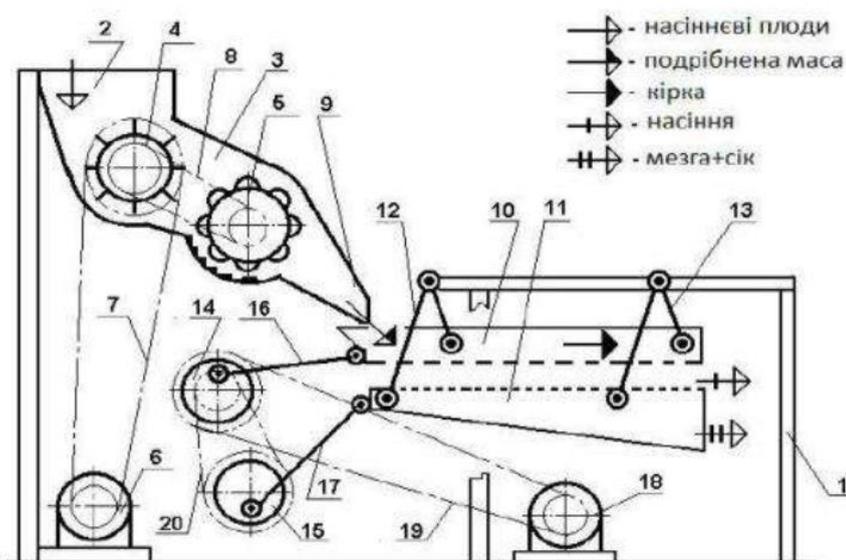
Конструктивна схема дослідного зразка сепаратора насіння овоче-баштанних культур: 1 – рама; 2 – приймальний бункер; 3 – подрібнювальна камера; 4 – подрібнювальний барабан; 5 – протиральний барабан; 6 – електродвигун; 7 – клинопасова передача; 8 – клинопасовий варіатор; 9 – лоток;
